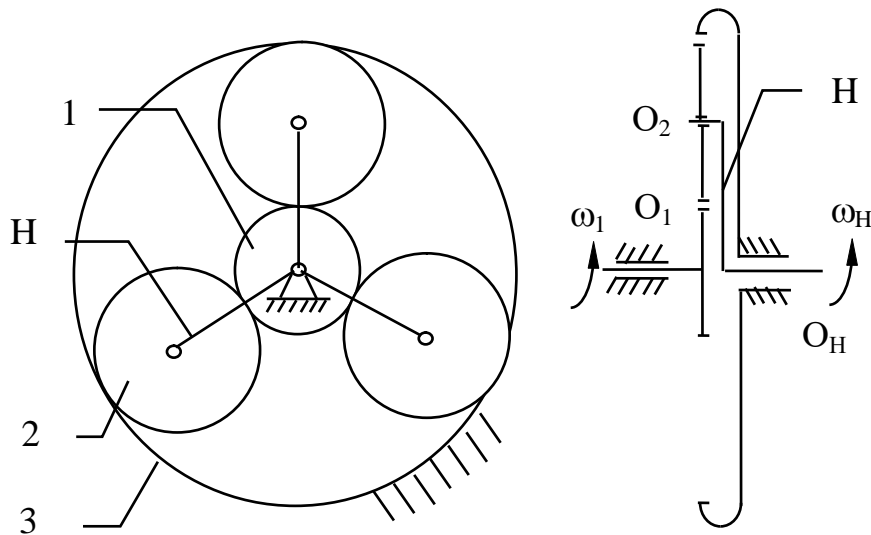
Схема планетарного механизма (редуктор Джеймса)
